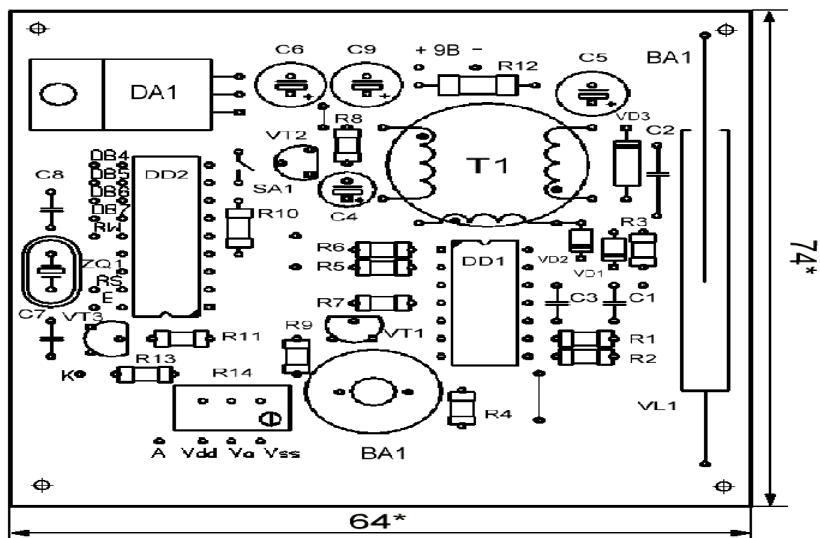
Сборочный чертеж печатной платы «Радон-222»
